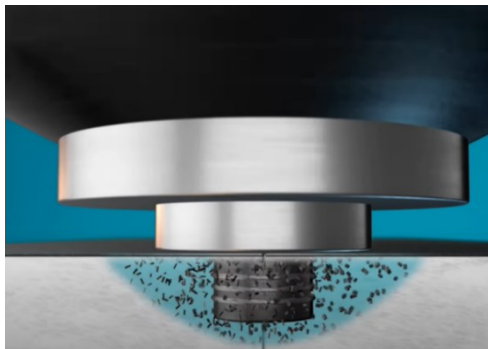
Mescolamento del materiale durante il processo di saldatura
